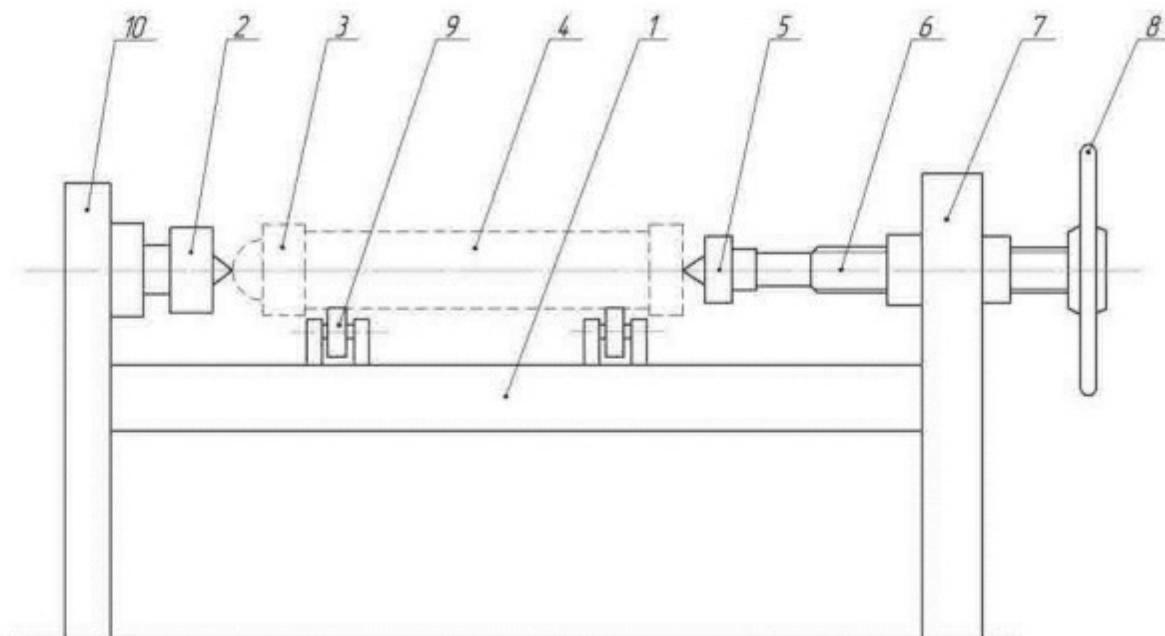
Стенд для сборки-сварки гидроцилиндров по А.с. №1773956.
